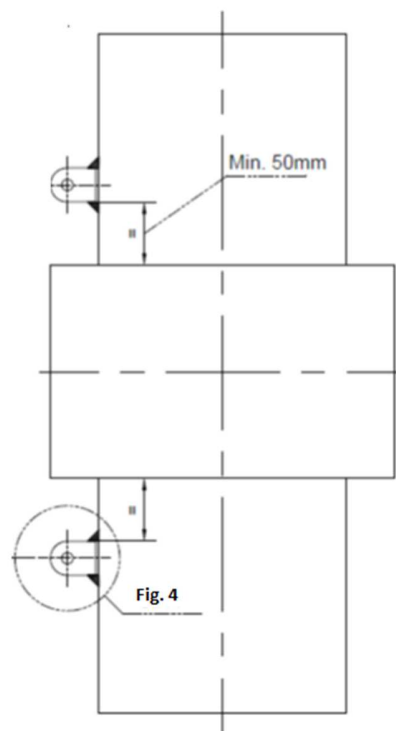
Olhais soldados a junta para instalação de DPS
